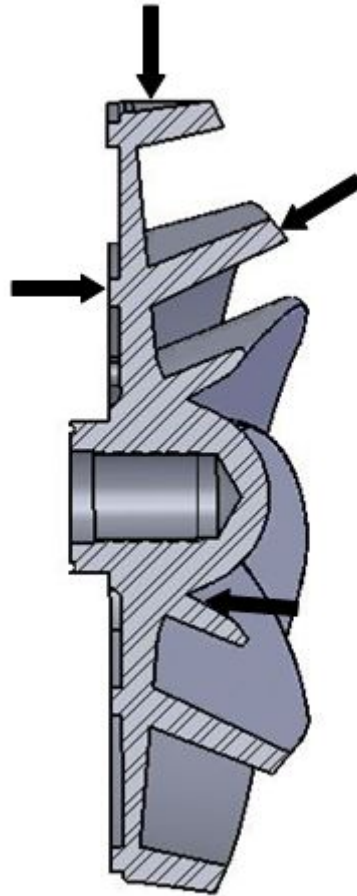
Áreas que se deben inspeccionar por desgaste en el impulsor de PWA-LF.
